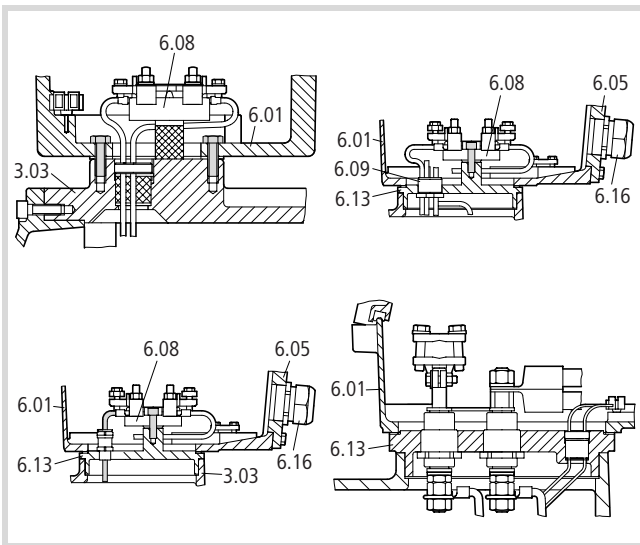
Klemmenkasten mit Schrauben befestigen
